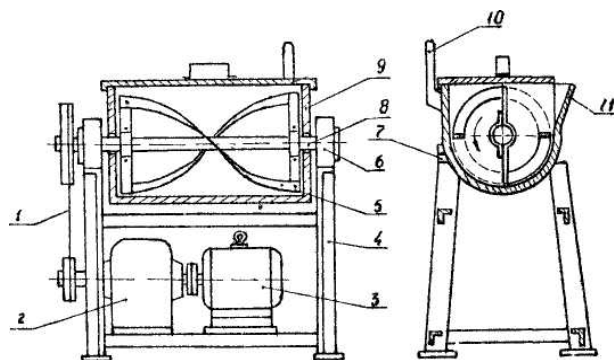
Шнековий лабораторний змішувач: 1 – клинопасова передача; 2 – редуктор; 3 – електродвигун; 4 – рама; 5 – лопаті; 6 – підшипники ковзання; 7 – упор; 8 – вал; 9 – корпус; 10 – рукоятка; 11 – лоток
